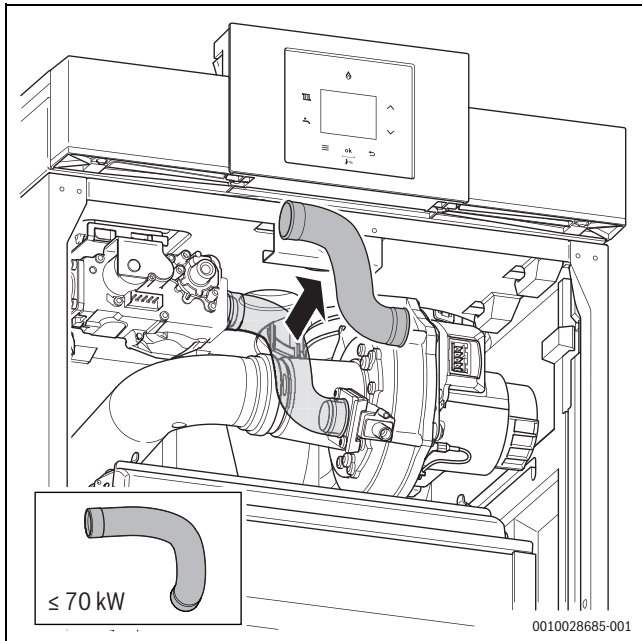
Remova a mangueira de gás ≥ 85 kW
